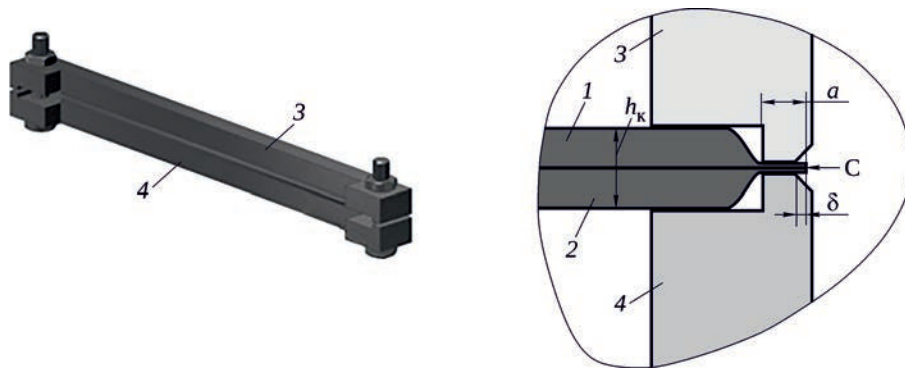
Приспособление для обжима свариваемых пластин и его геометрия:
